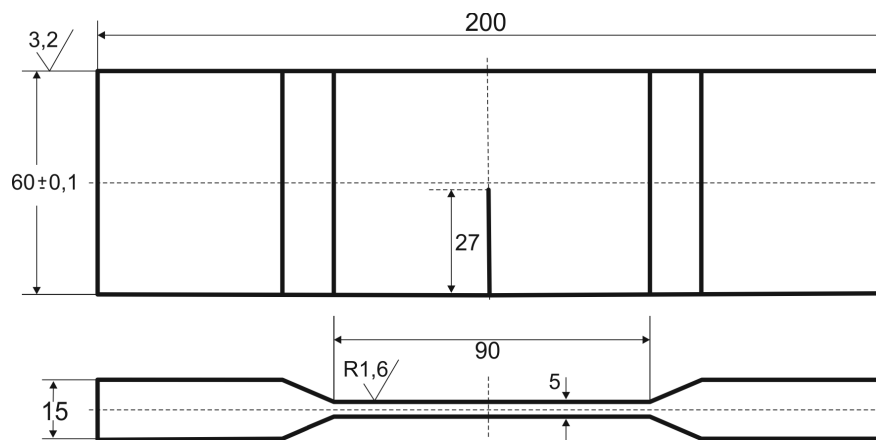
Technische Zeichnung der Stahlproben mit erodierter Seitenkerbe
